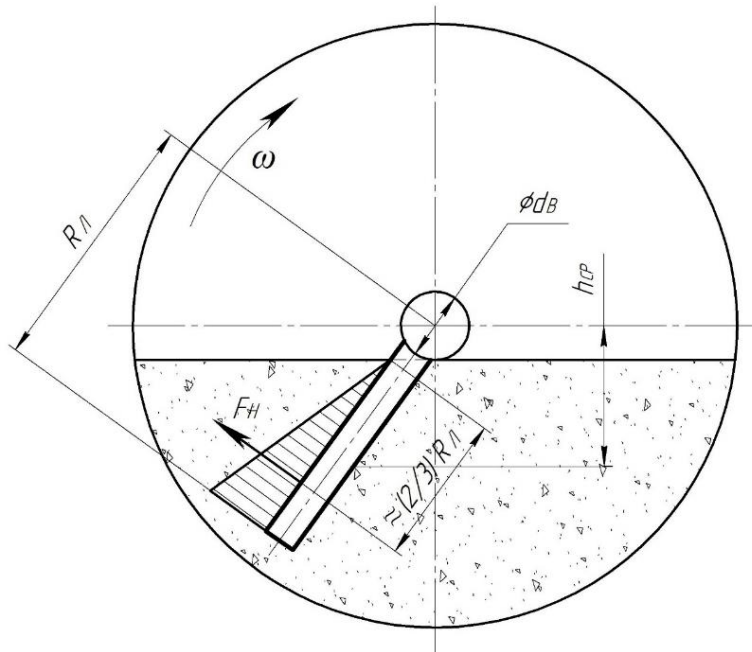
Розрахункова схема лопатевого змішувача
